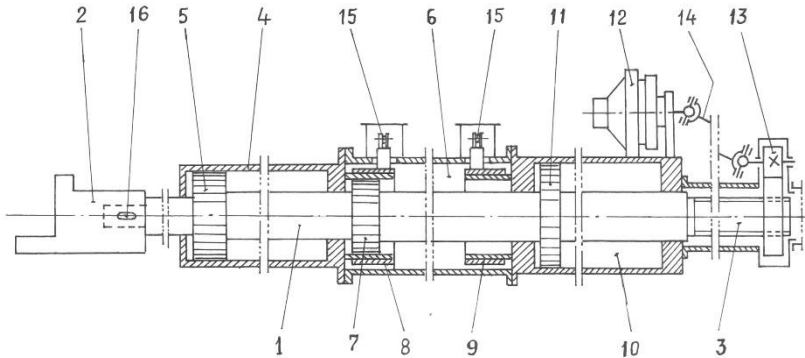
Схема подавального апарата фірми ITWH (Німеччина): 1 – полий шток; 2 – дорнотримач; 3 – шліцьовий вал; 4 – напрямний циліндр; 5 – опорний барабан; 6 – гальмівна масляна камера; 7 – гальмівний поршень; 8, 9 – втулки гальмування; 10 – повітряний циліндр; 11 – поршень повітряного циліндра; 12 – гідромотори (два) привода кантування гільзи; 13 – зубчата передача; 14 – карданний вал; 15 – привод повороту обійми регулювання; 16 – клинове з'єднання.
